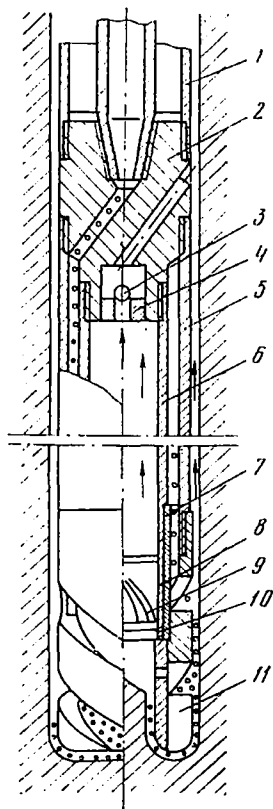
Двойной колонковый снаряд дробового бурения ДКСД-1 конструкции КазИМСа.
